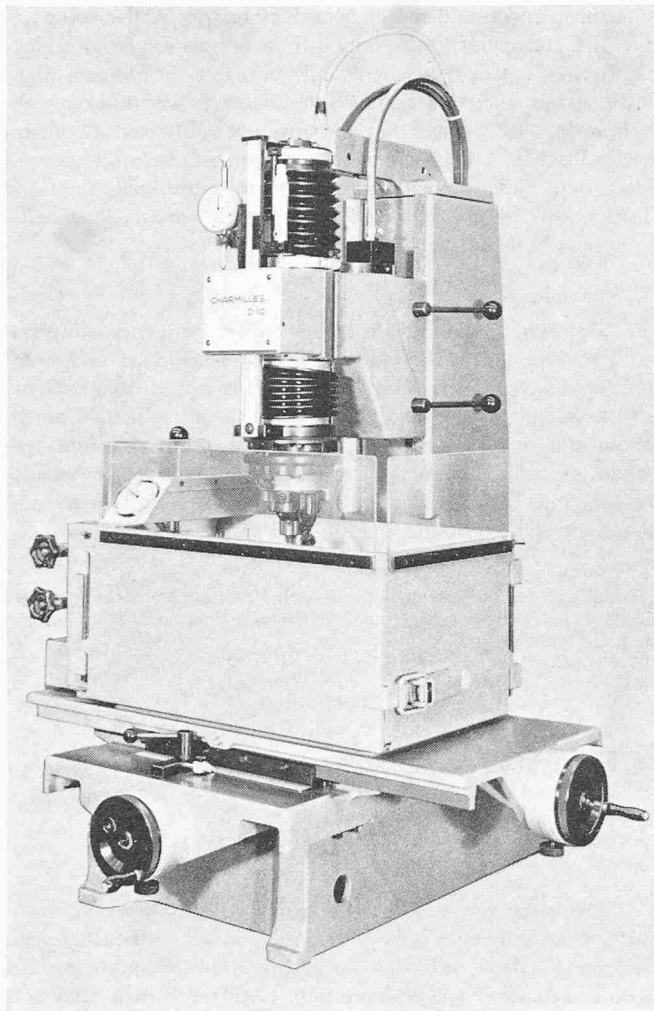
Funkerosions-Werkzeugmaschine Charmilles D 10
